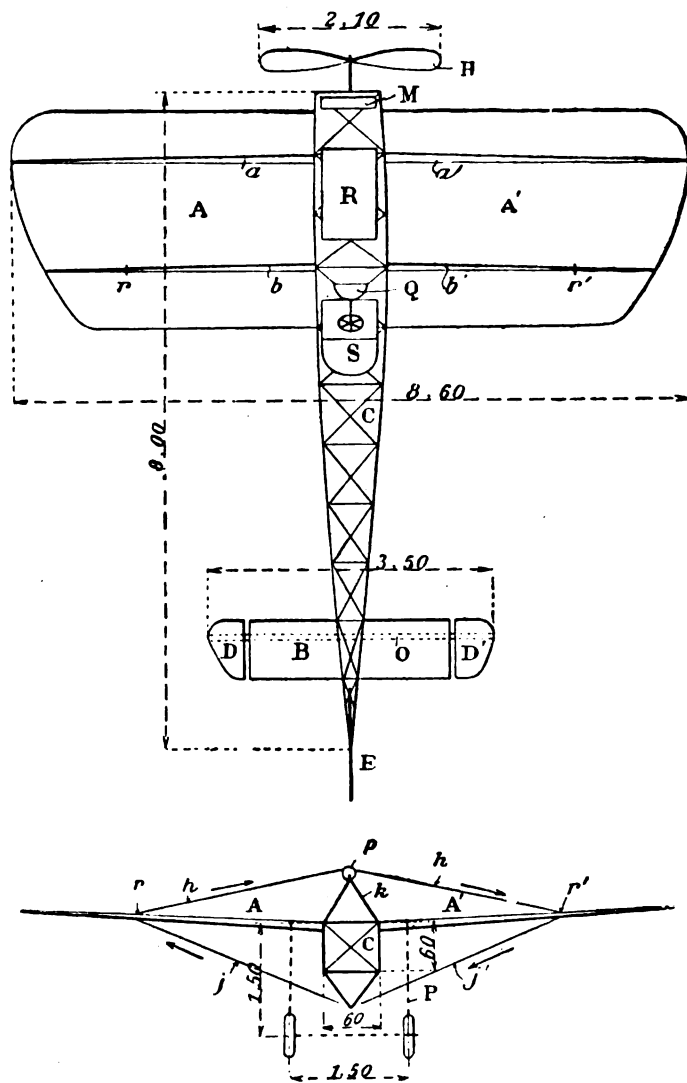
Monoplano Blériot - Pianta e sezione.
